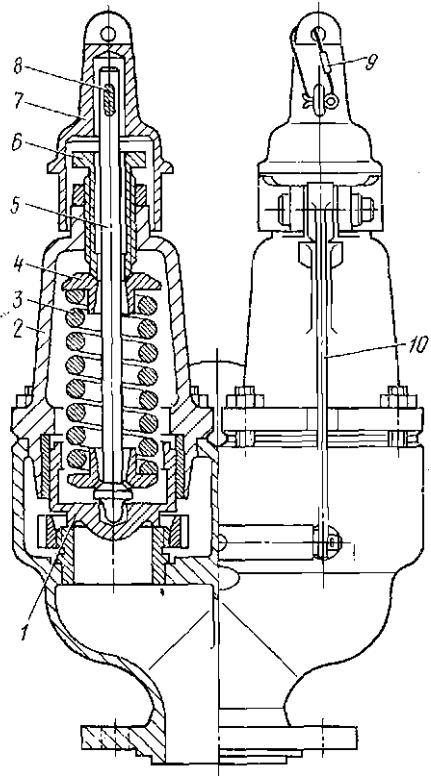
Двудействующий прямодействующий предохранительный клапан
